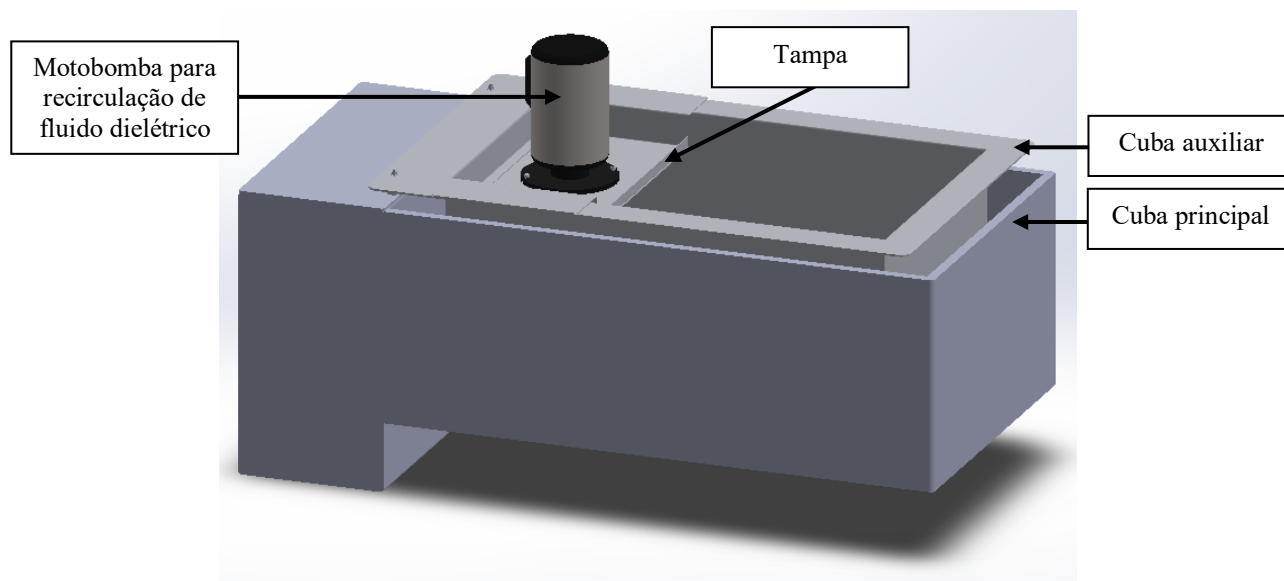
Representação da cuba auxiliar, tampa e motobomba de recirculação para novo fluido dielétrico.
